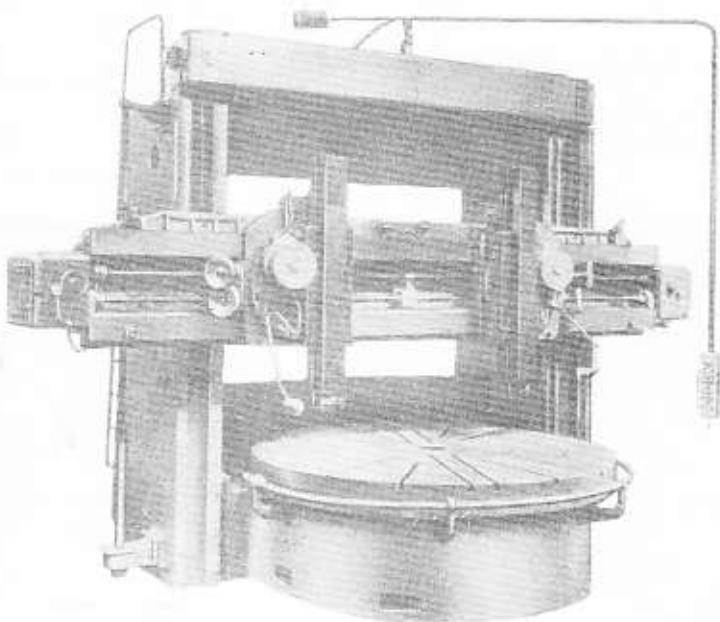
Рис. I. Универсальный двухстоечный токарно-карусельный станок IM557
